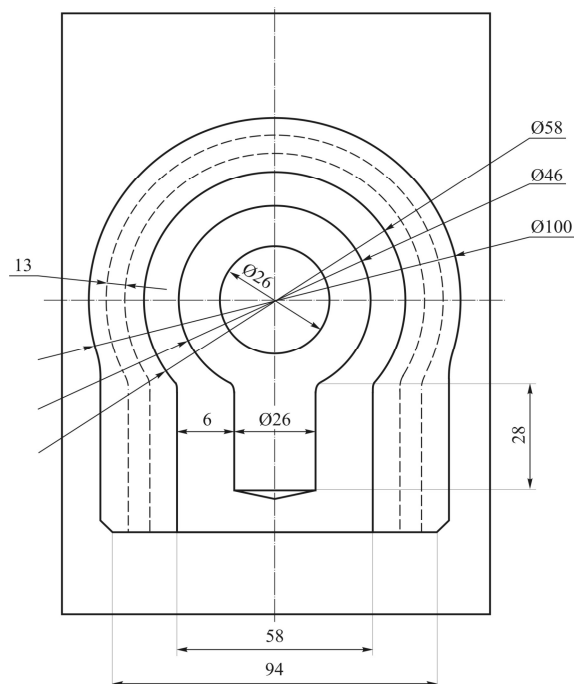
Эскиз гравюры штампа для штамповки поковки «рым - болт»
